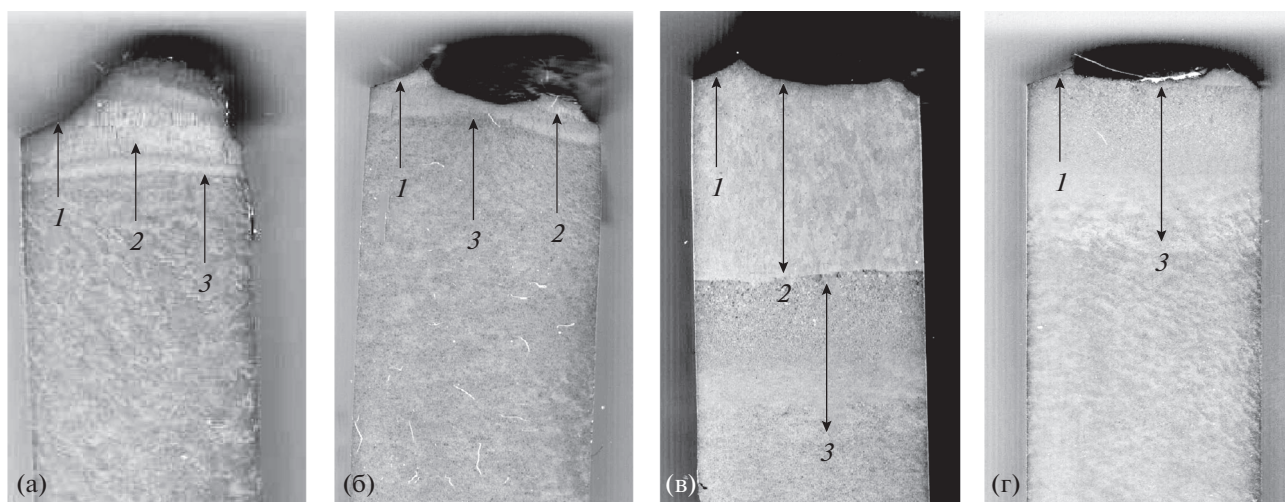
Макроструктура фрагментов образцов сварных соединений после ударных испытаний: а, б – комбинированная технология сварки с надрезом по металлу шва ГЛДС (а), по линии сплавления шва ГЛДС (б.); в, г – стандартная технология сварки с надрезом по металлу шва ДСФ (в), по линии сплавления шва ДСФ (г). Цифрами обозначены: 1 – надрез; 2 – металл шва; 3 – зона термического влияния сварного шва.
